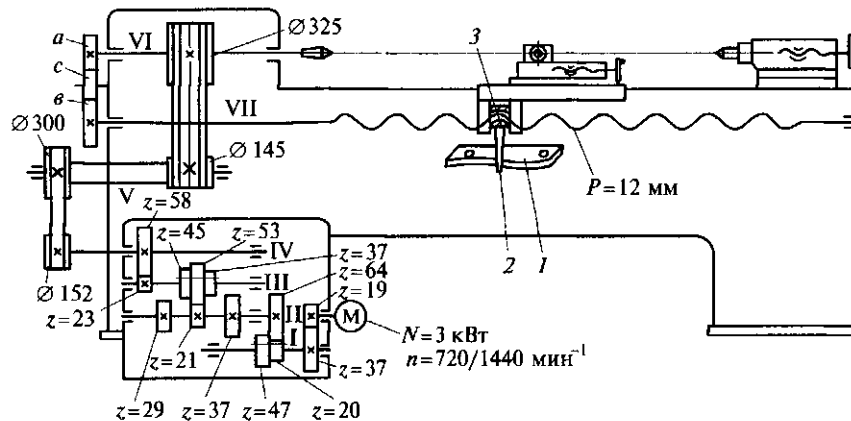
Кинематическая схема специализированного винторезного станка:
